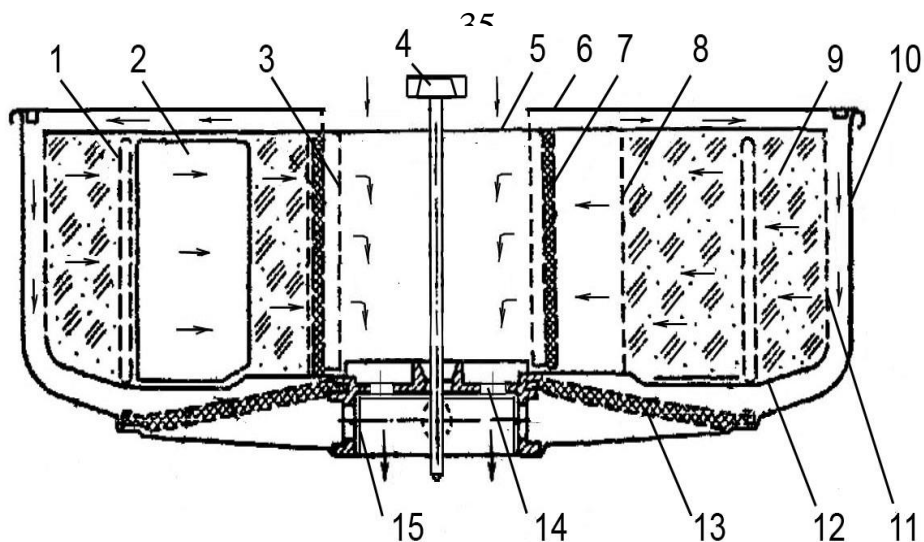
2 – Схема регенеративного патрона, усовершенствованного с центростремительным движением воздушного потока
